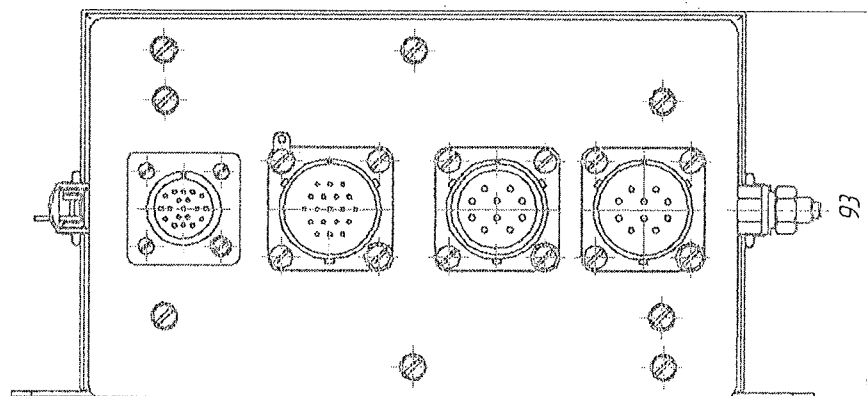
Внешний вид и габаритные размеры блока
